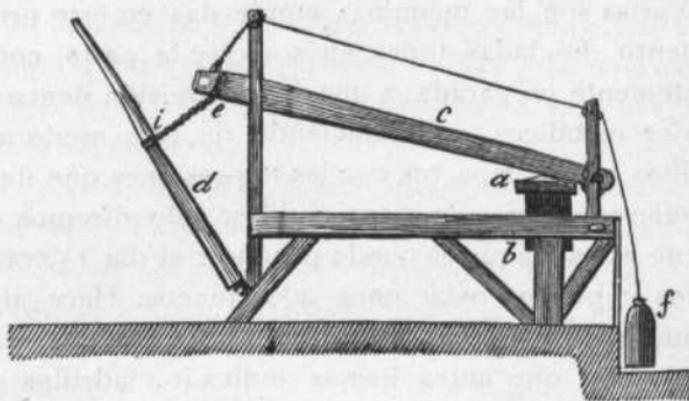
Prensa antigua de moldear ladrillos a brazo.
